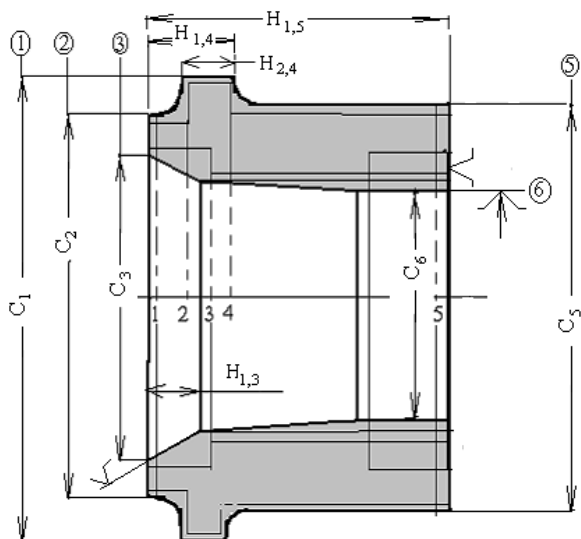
Эскиз заготовки «Коронная шестерня»
